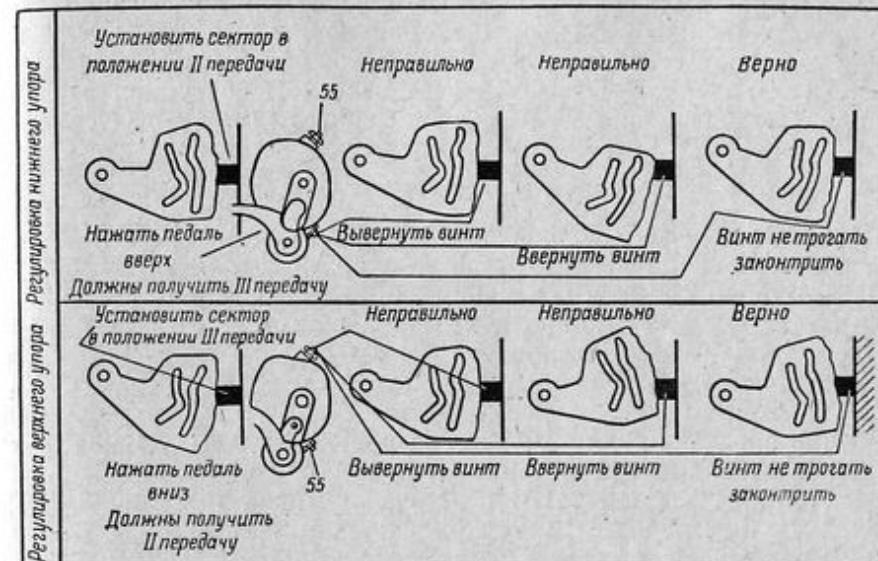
Регулировка коробки перемены передач мотоцикла М-72:
